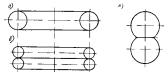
Форма камер спасательных плотов: а — цилиндрическая; б, в — шаровидная.
